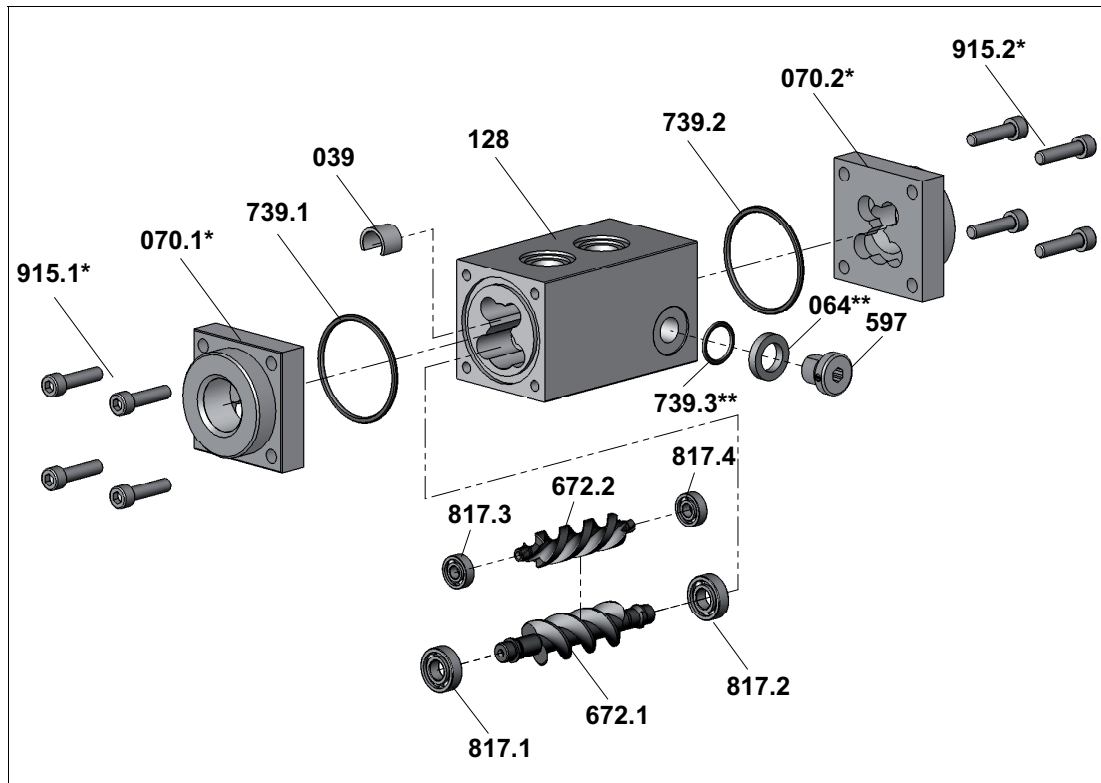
Explosionszeichnung OME 13 / 20 / 32 / 52
